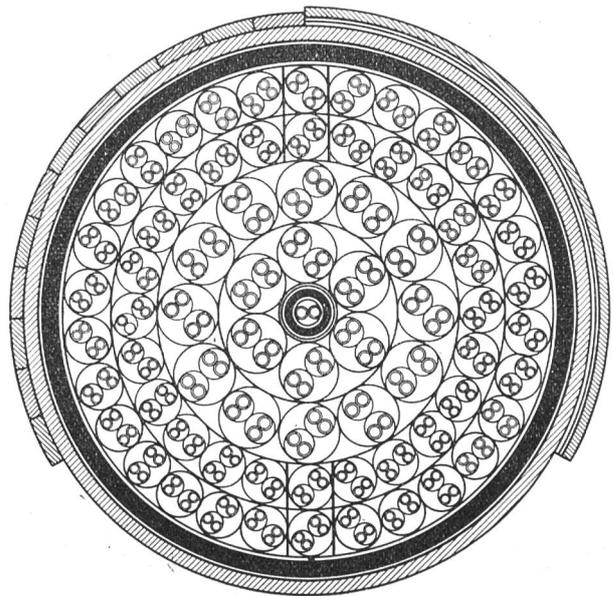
Querschnitt des Kabels mit 72 Vierern.
